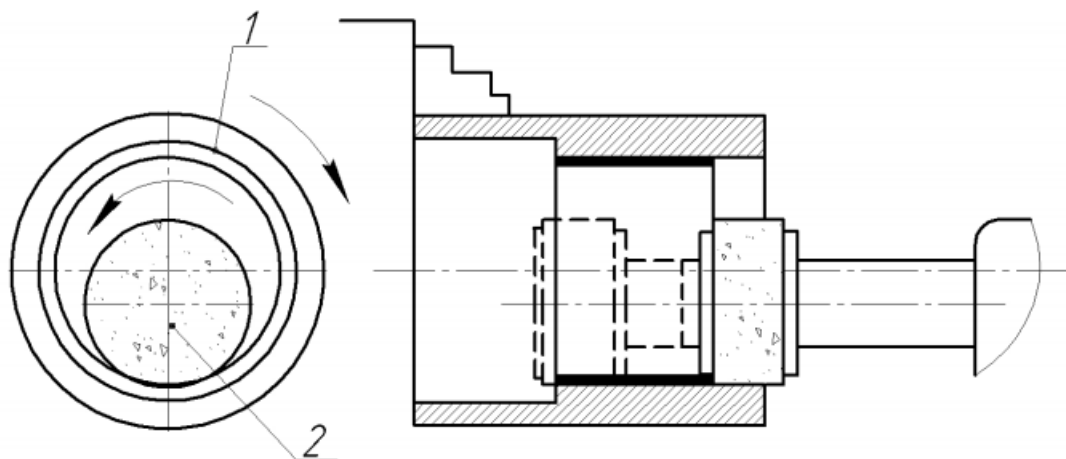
Схема обробки отвору на внутрішньо-шліфувальному верстаті
